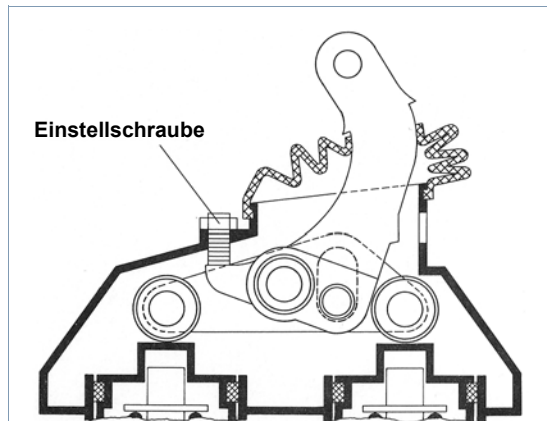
Motorwagen-Bremsventil 461 499 - Querschnitt, Position der Einstellschraube
